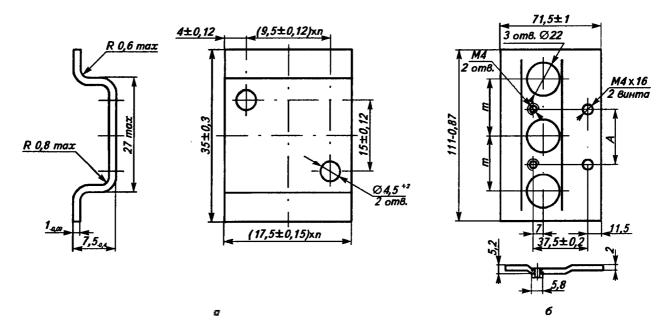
Чертеж рейки для крепления выключателей n- количество выключателей, устанавливаемых на рейке; a- центральная рейка; b- рейка для выключателей с закрытым пазом
